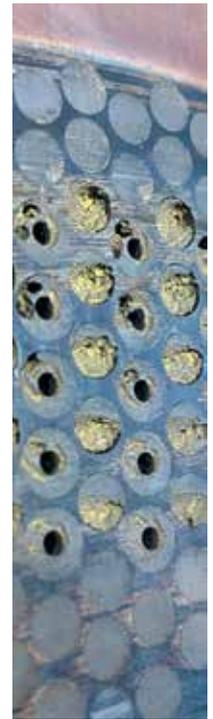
Ein Säureangriff hat die Schneidfläche dieser Lochplatte schwer beschädigt.
